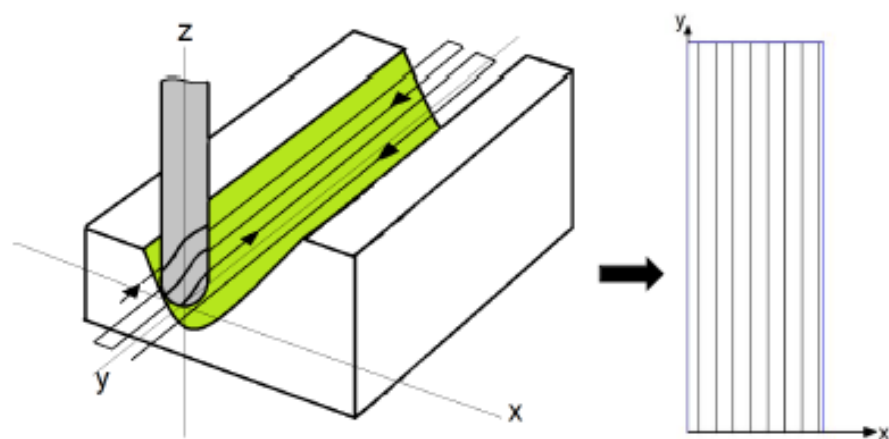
Схема фрезерування з траєкторією, розташованою вздовж формоутворюючої поверхні
